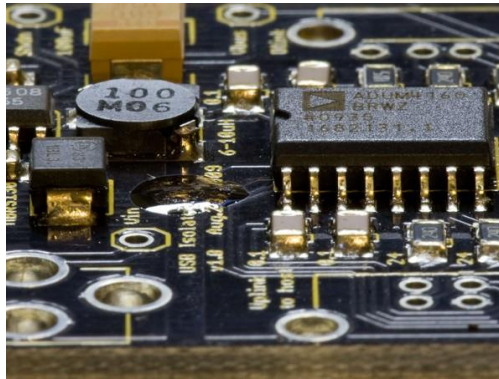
PCB tras ser sometida a un proceso de soldadura blanda por reflujo. Tomada de[27].
